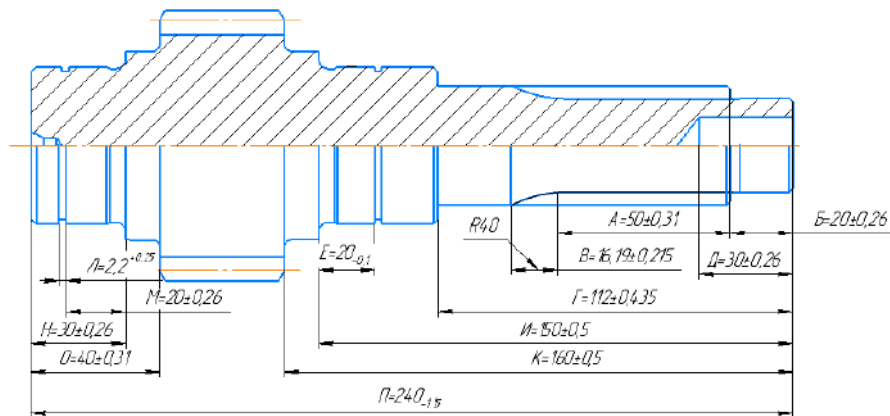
Преобразованный чертёж детали в первой проекции
